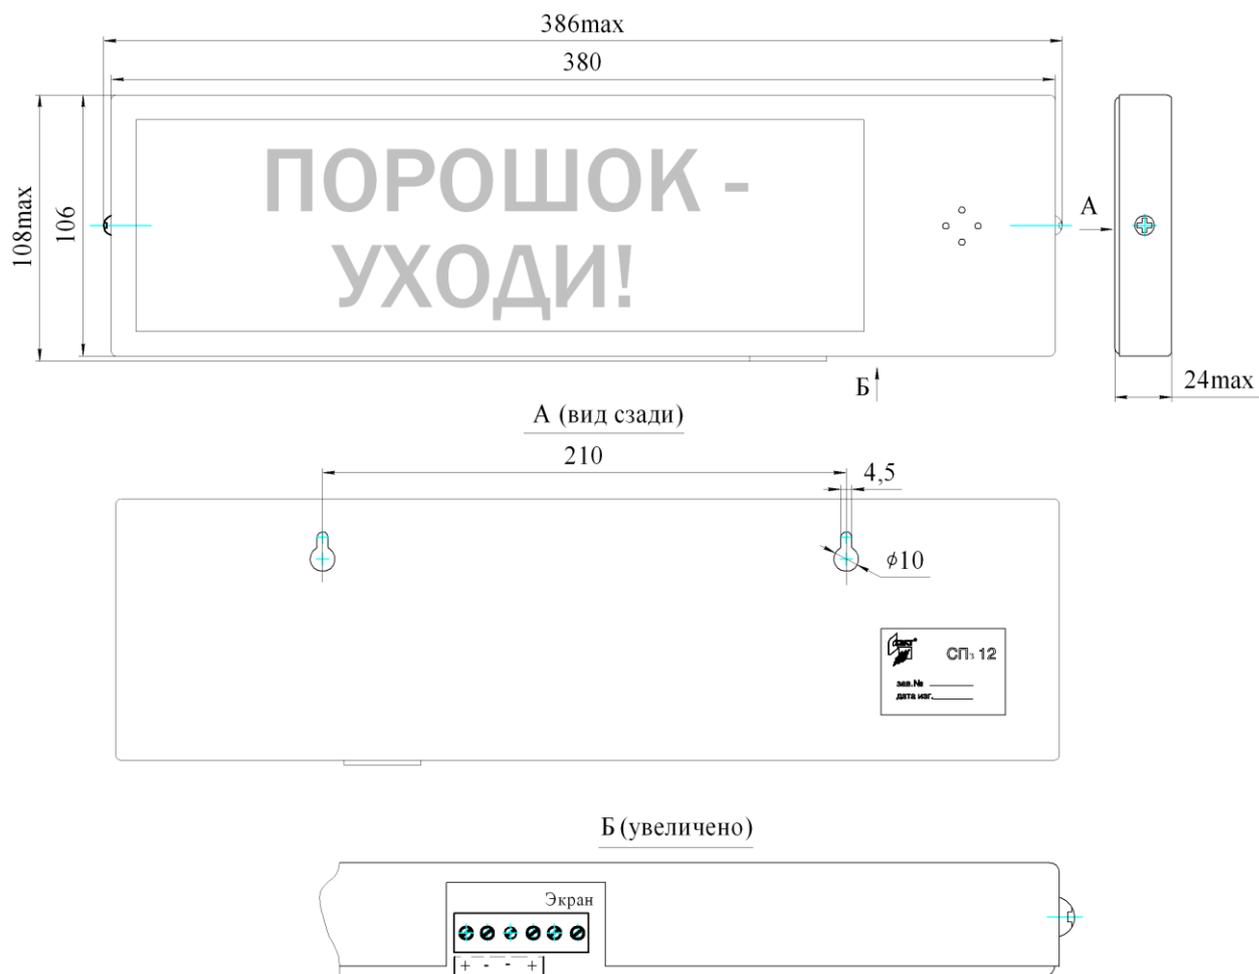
Оповещатель СПз 12. Габаритный чертёж
